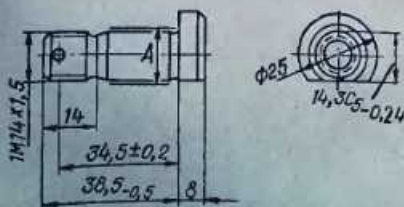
Болт для соединения коленчатого вала с амортизатором
